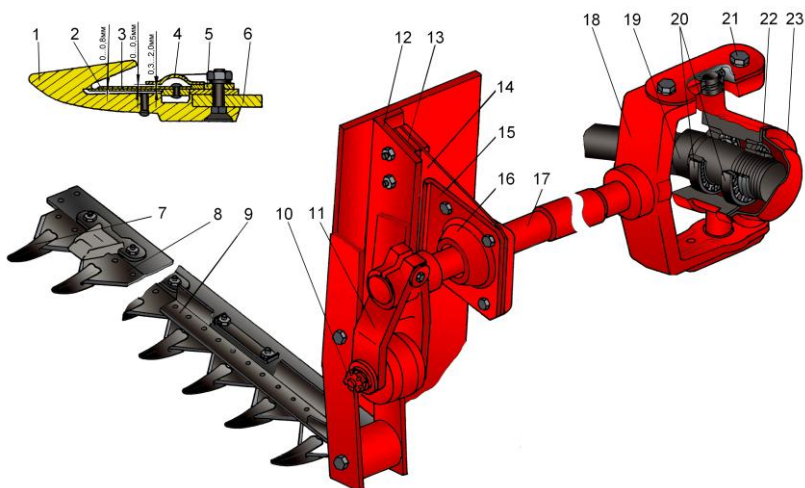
Механизм «качающейся шайбы»: 1 – палец; 2 – противорезущая пластина; 3 – сегмент; 4 – прижим; 5 – регулировочная прокладка; 6 – пластина трения; 7 – пальцевый брус; 8 – нож; 9 – головка ножа; 10 – ось; 11 – вилка; 12 – уголок; 13 – регулировочные прокладки; 14 – кронштейн; 15 – промежуточная опора; 16 – корпус; 17 – вал колебателя; 18 – вилка колебателя; 19 – кривошипный вал; 20 – роликовый конический подшипник; 21 – болт; 22 – корпус; 23 – крышка
